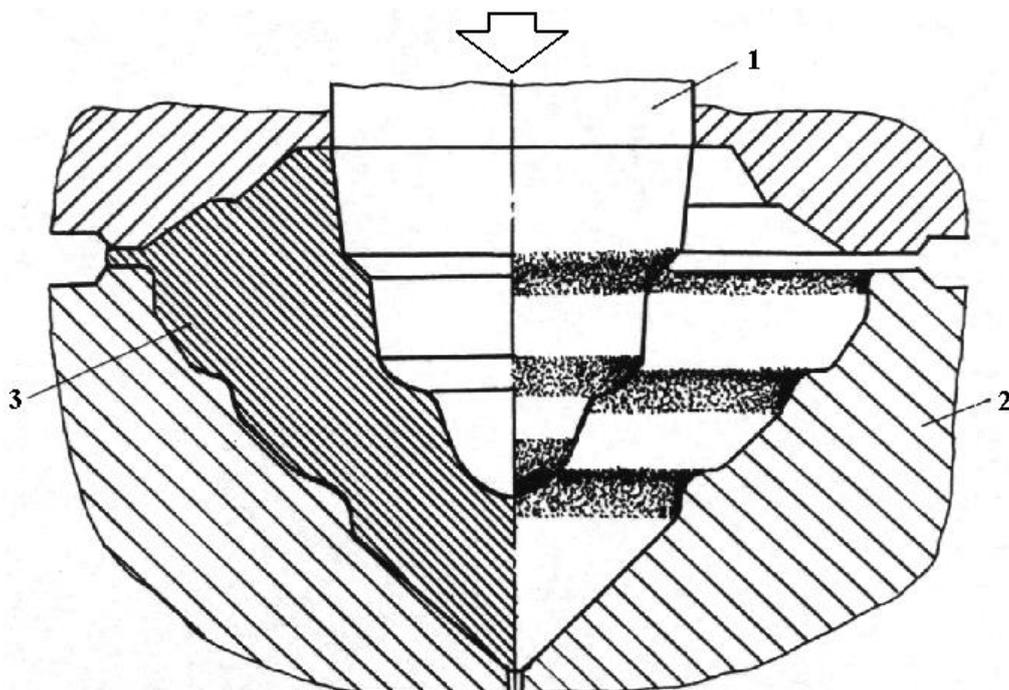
Зоны нанесения упрочняющих покрытий на рабочие части штампа для штамповки “шарошки”.
